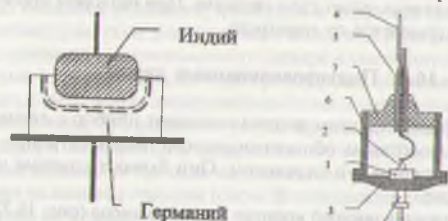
Плоскостный германиевый диод: 1-кристалл германия; 2-кристалл индия; 3-кристаллодержатель; 4-верхний и нижний зажимы; 5-внутренний зажим; 6-металлический корпус; 7-стеклянный изолятор.
